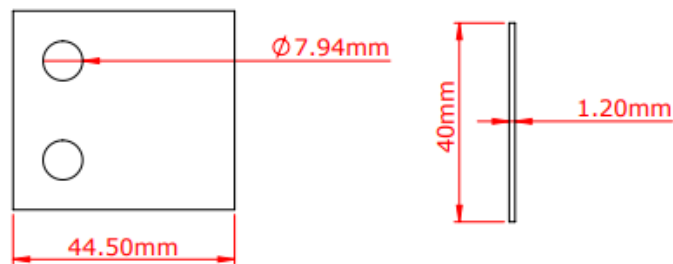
Sección 3 de la cuchilla circular - Detalle de las dimensiones
